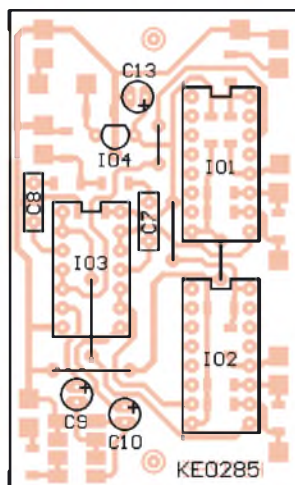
Obrazec plošných spojů testeru krystalů (měř.: 1 : 1)
